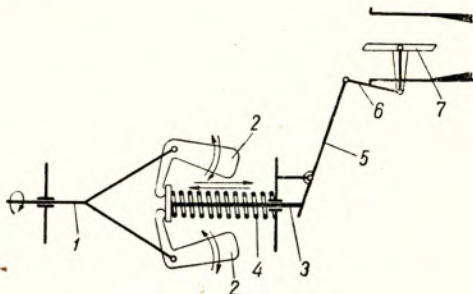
Схема центробежного регулятора двигателей Л-3/2 и Л-6/3
